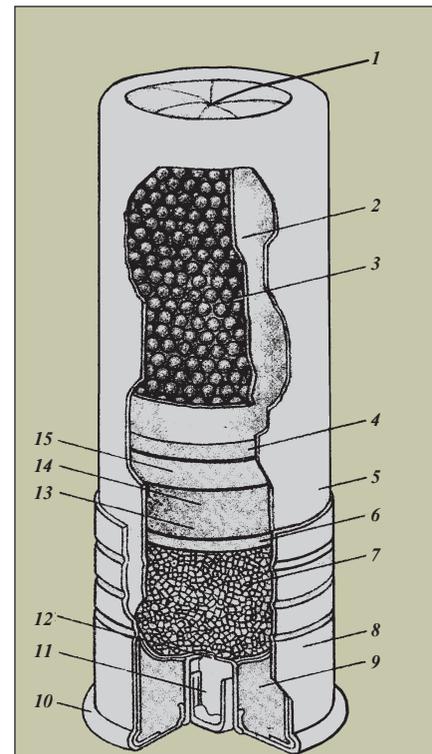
Устройство дробового патрона: 1 — опрессовка «звездочкой»; 2 — контейнер (концентратор); 3 — дробь; 4, 6, 14, 15 — пыжи и прокладки; 5 — корпус гильзы; 7 — порох; 8 — основание гильзы; 9 — поддон; 10 — фланец гильзы; 11 — капсюль; 12 — запальное отверстие; 13 — осалка основного пыжа
